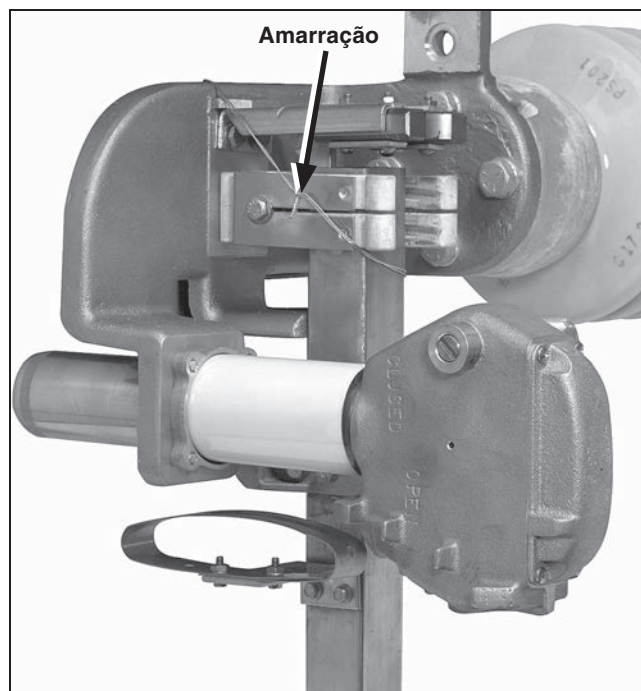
Remova a amarração no conjunto do contato fixo principal.
